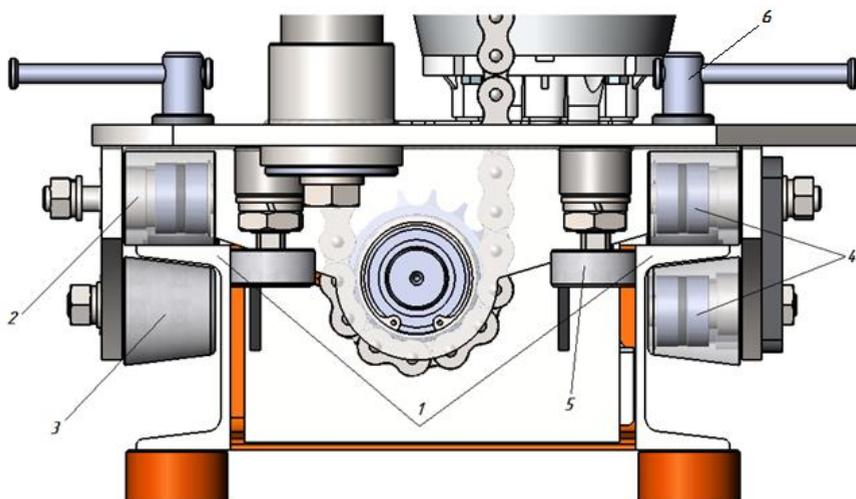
Роликовый механизм перемещения буровой мачты: 1 – направляющие швеллеры; 2 – верхний ролик; 3 – нижний ролик; 4 – шариковые подшипники роликов; 5 – боковой ролик; 6 – зажим
